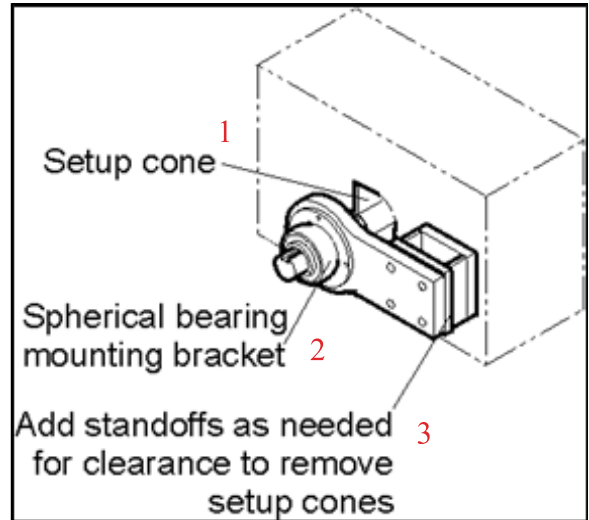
INSTALLATION DES CÔNES D'INSTALLATION
